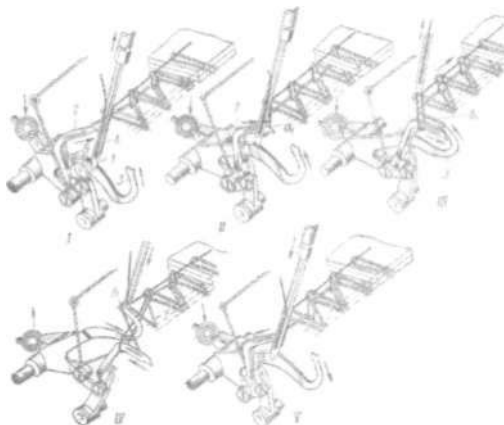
Процесс образования двухниточного цепного обметочного стежка
